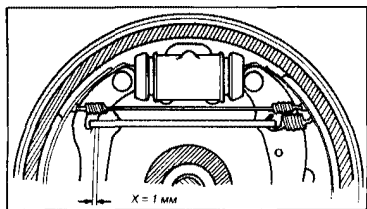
Зазор распорной планки — тормоза типа Bendix
